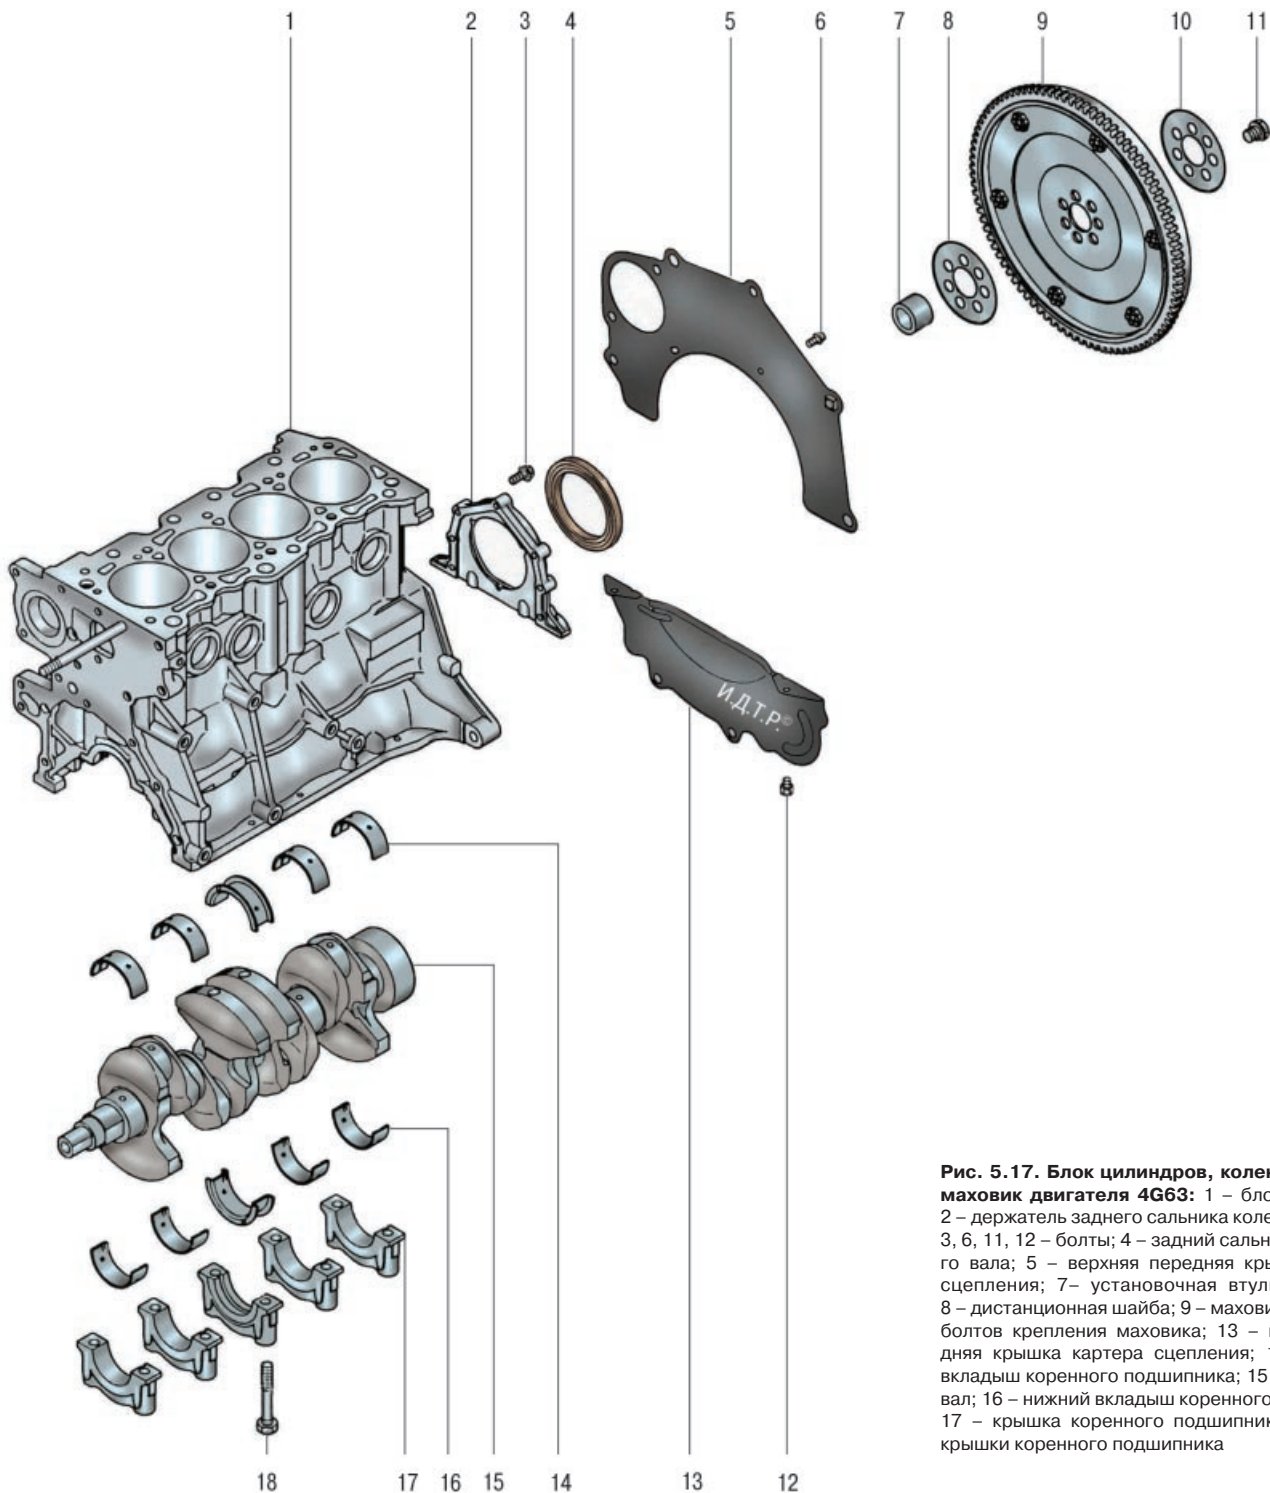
Блок цилиндров, коленчатый вал и маховик двигателя 4G63: 1 – блок цилиндров; 2 – держатель заднего сальника коленчатого вала; 3, 6, 11, 12 – болты; 4 – задний сальник коленчатого вала; 5 – верхняя передняя крышка картера сцепления; 7 – установочная втулка маховика; 8 – дистанционная шайба; 9 – маховик; 10 – шайба болтов крепления маховика; 13 – нижняя передняя крышка картера сцепления; 14 – верхний вкладыш коренного подшипника; 15 – коленчатый вал; 16 – нижний вкладыш коренного подшипника; 17 – крышка коренного подшипника; 18 – болт крышки коренного подшипника
